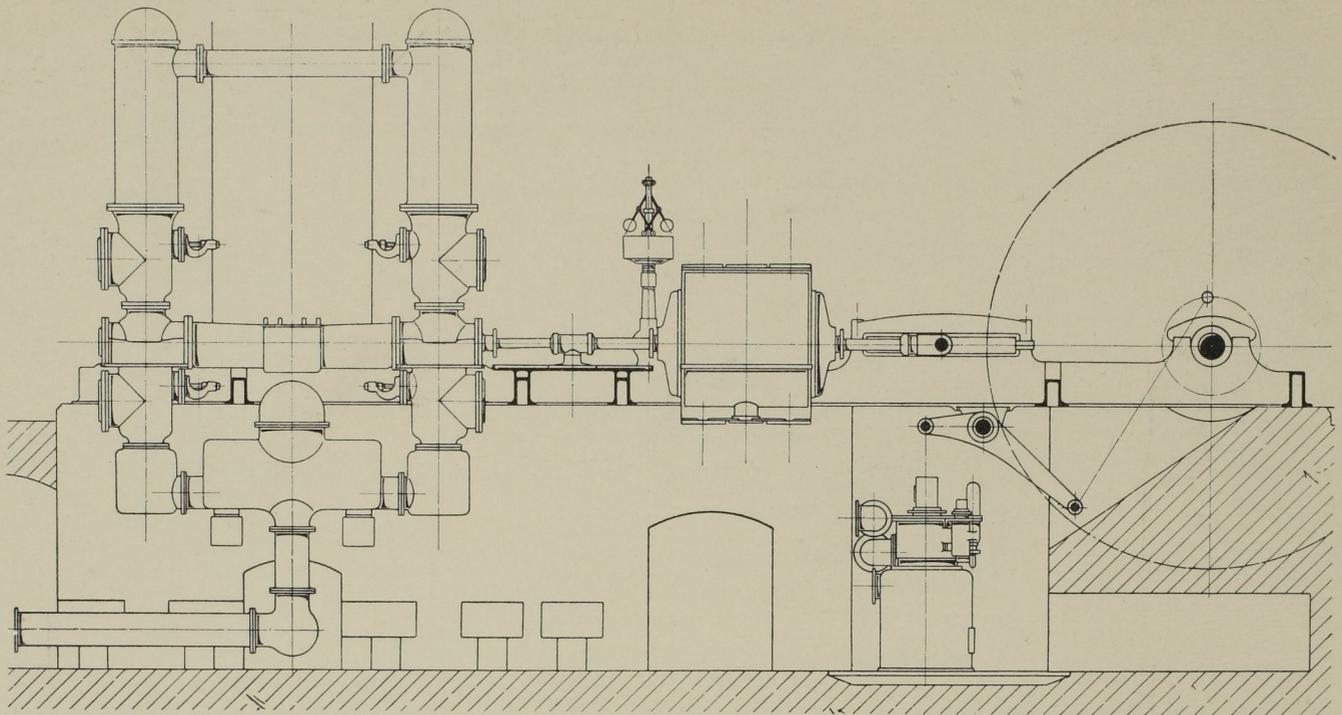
Seitenansicht der Pumpmaschine. Massst. 1:80.
